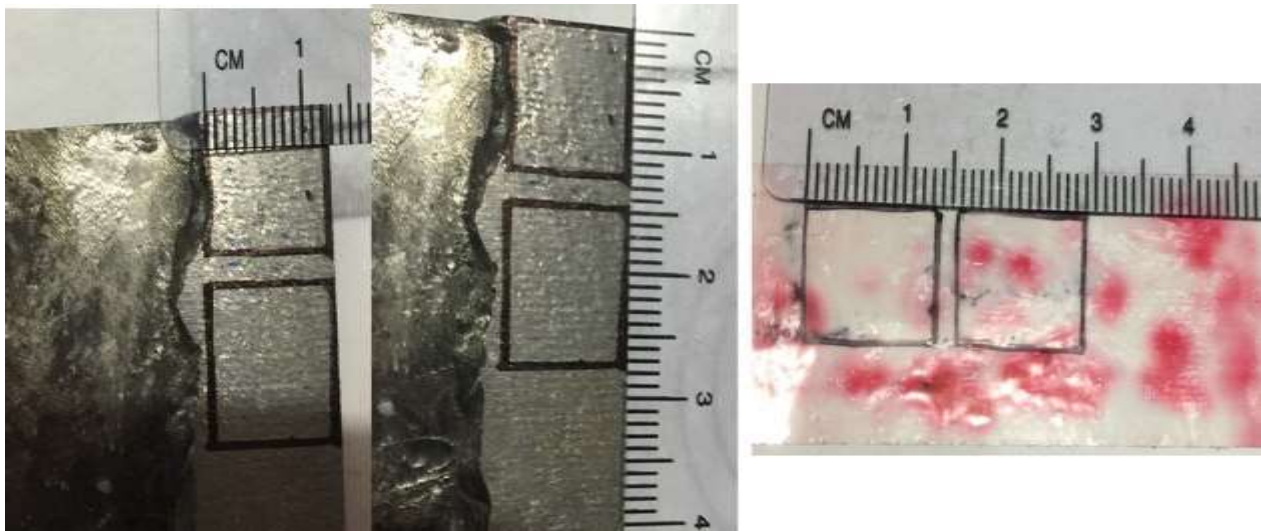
6 Método de medición de poros utilizando líquidos penetrantes sobre los insertos de acero H13 soldados
